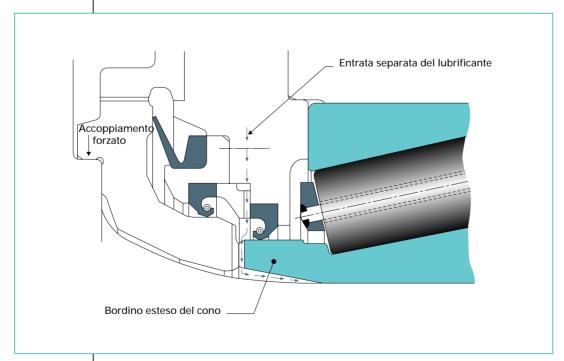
Lubrificazione del collo e dello spallamento attraverso intagli sulla faccia del cono
